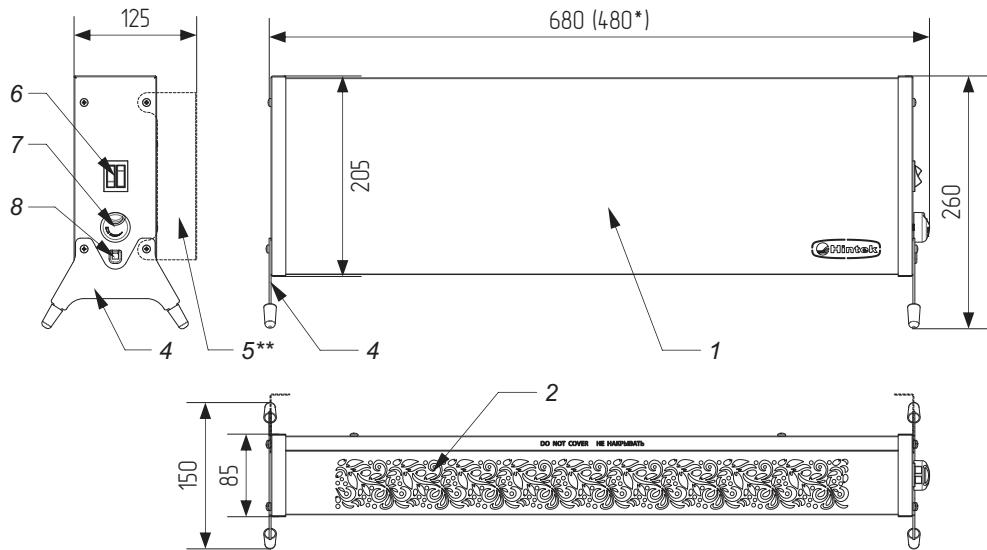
Габаритный чертёж и элементы конструкции электрического обогревателя.
